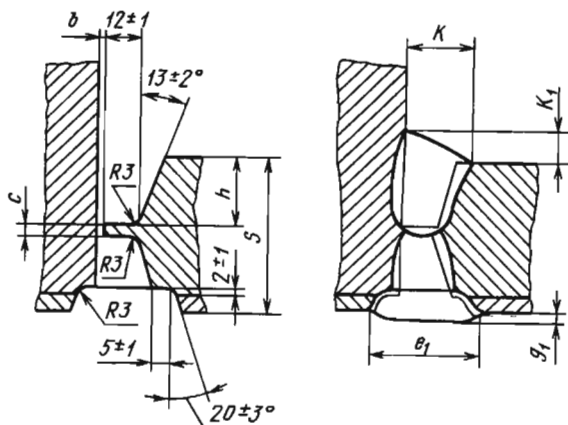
Разделка кромок и сварное угловое соединение двухслойной стали (У6)
